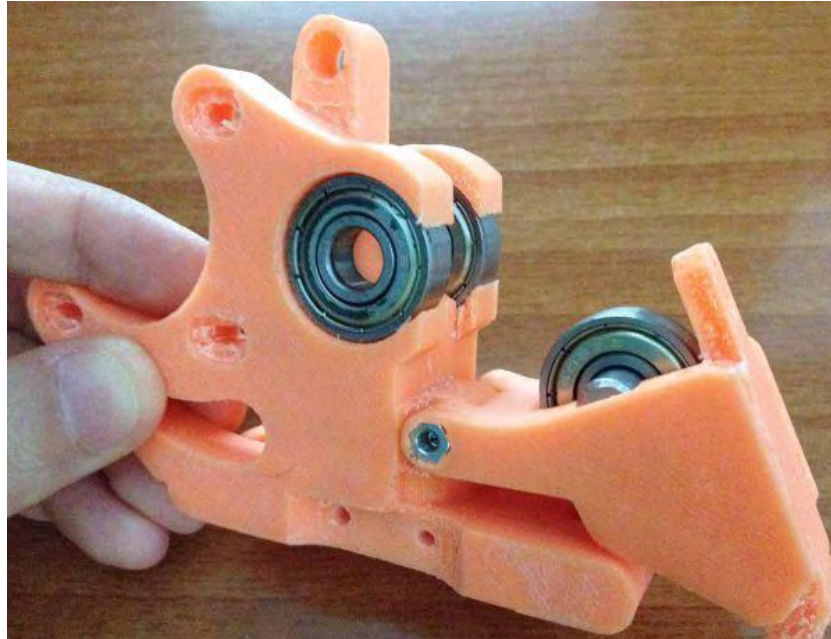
Cuerpo de extrusor con rodamientos y varilla
